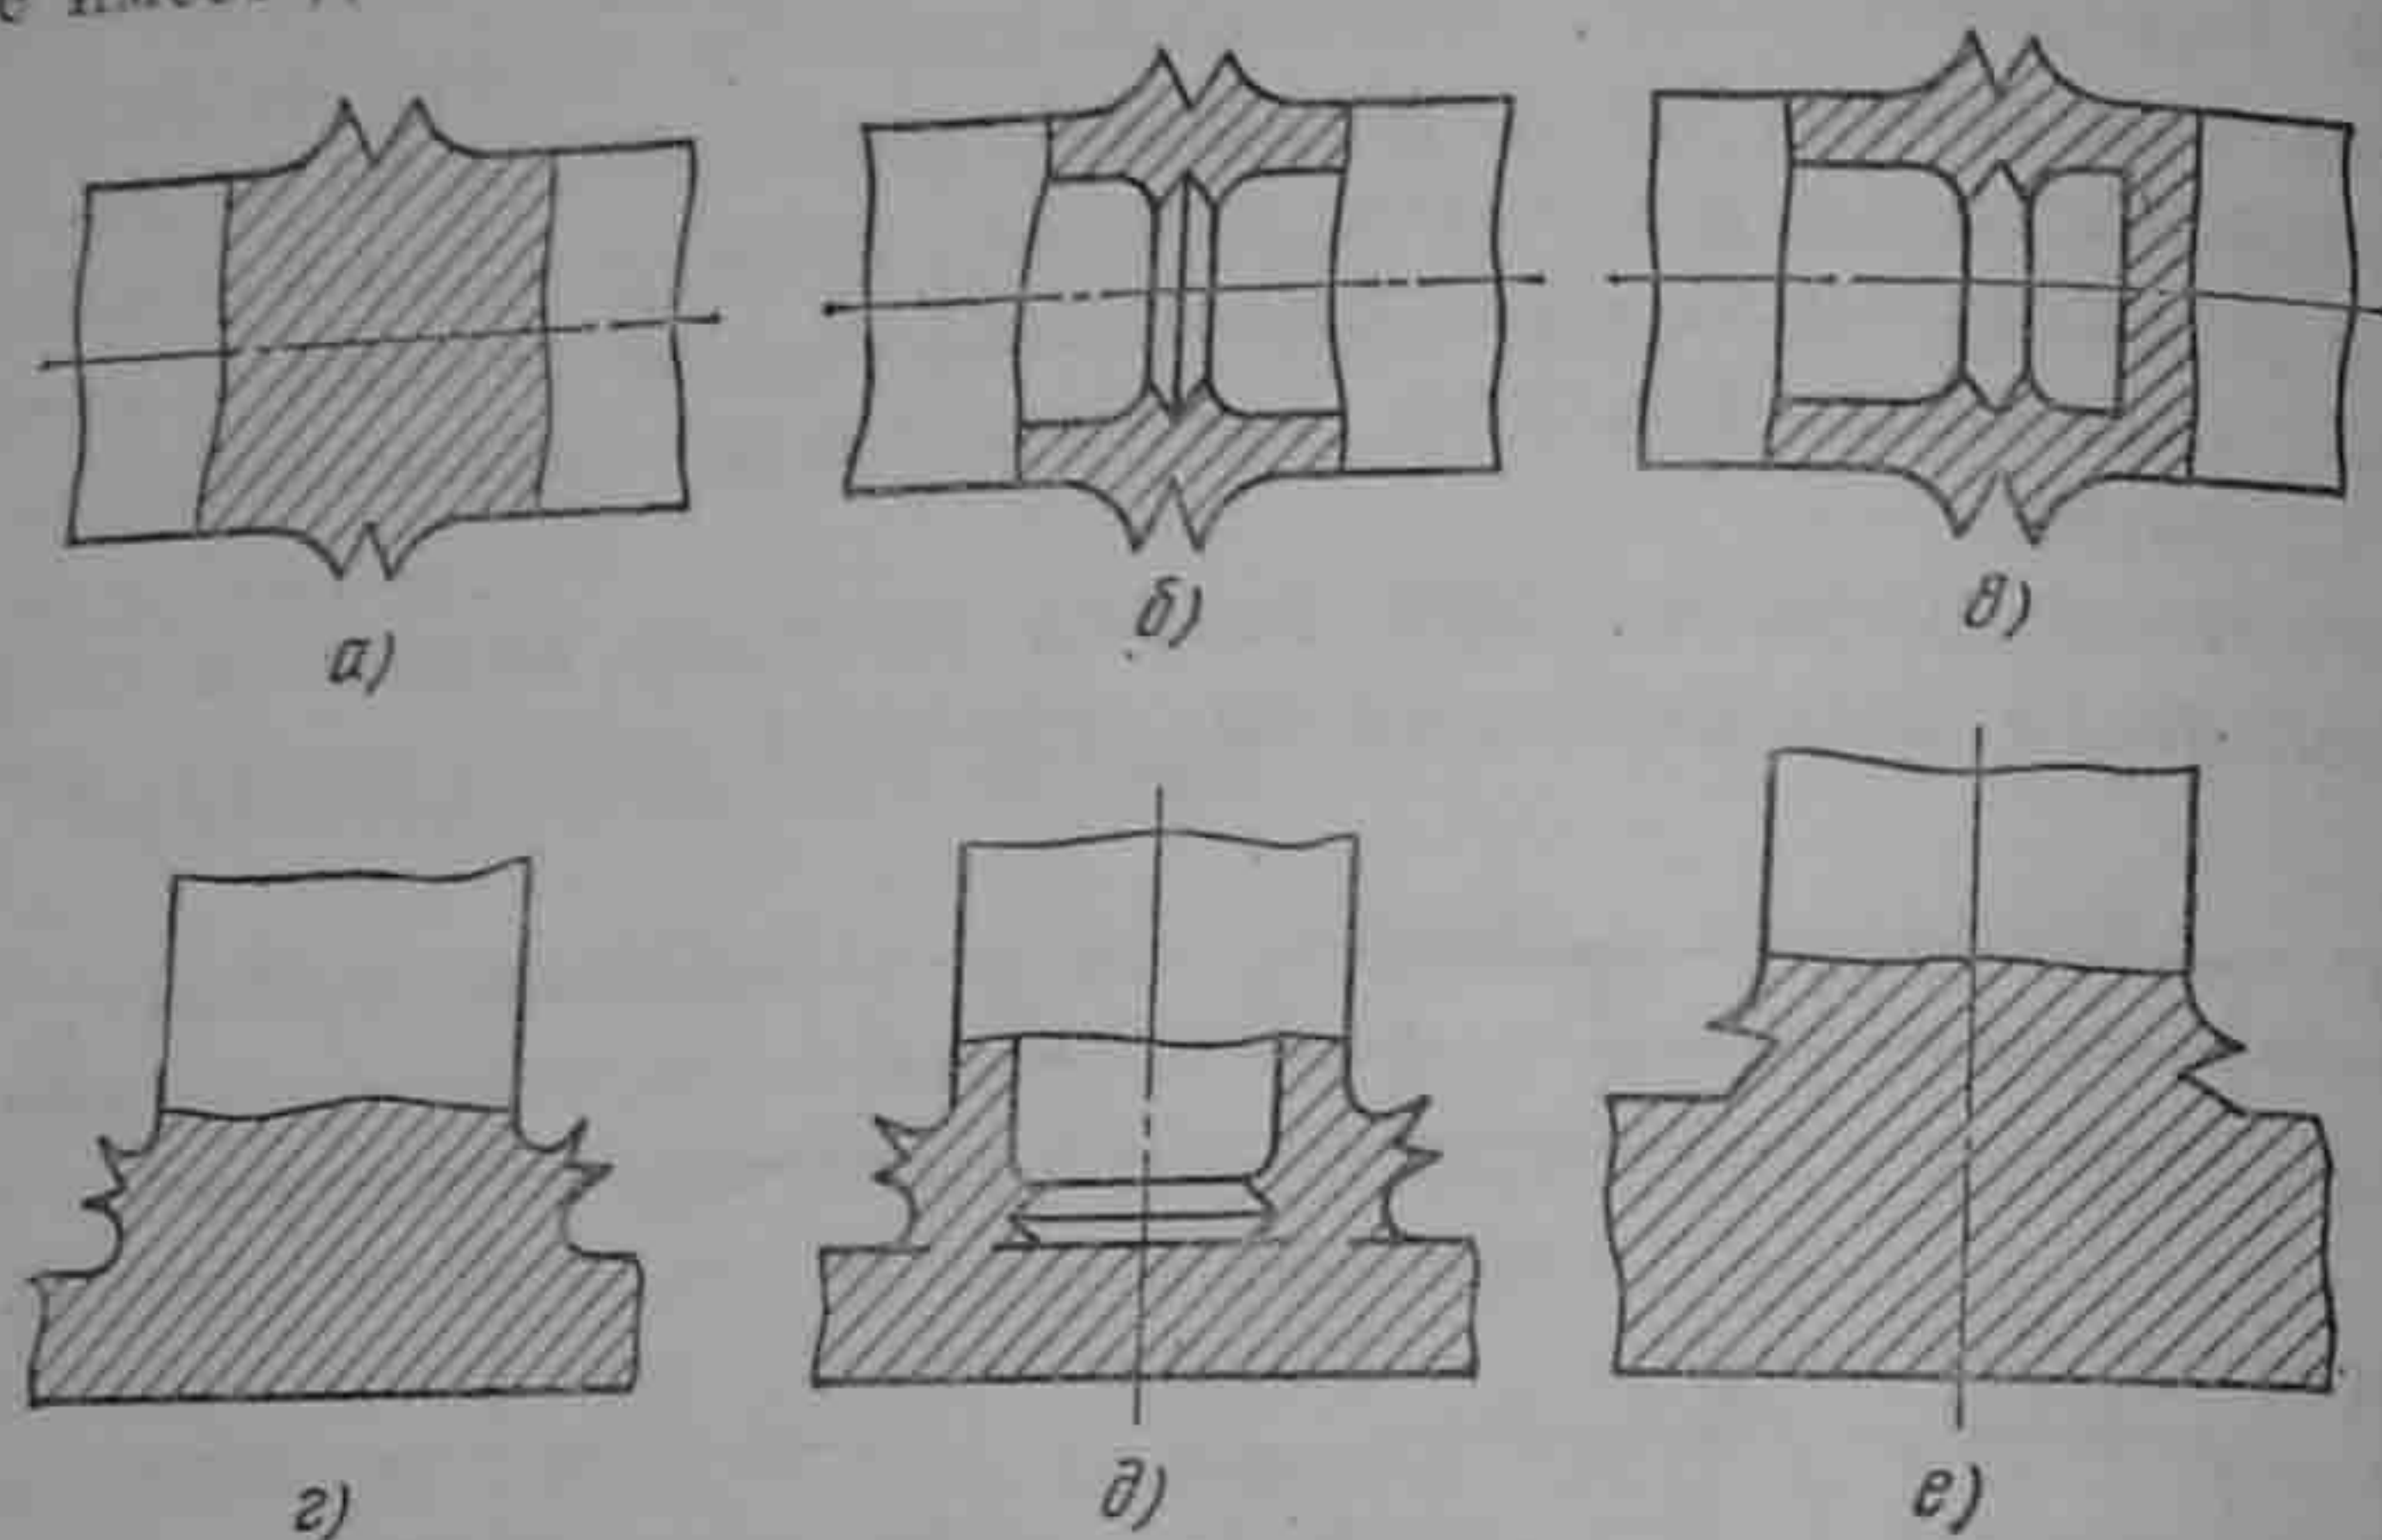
Типы сварных соединений сварки трением:
